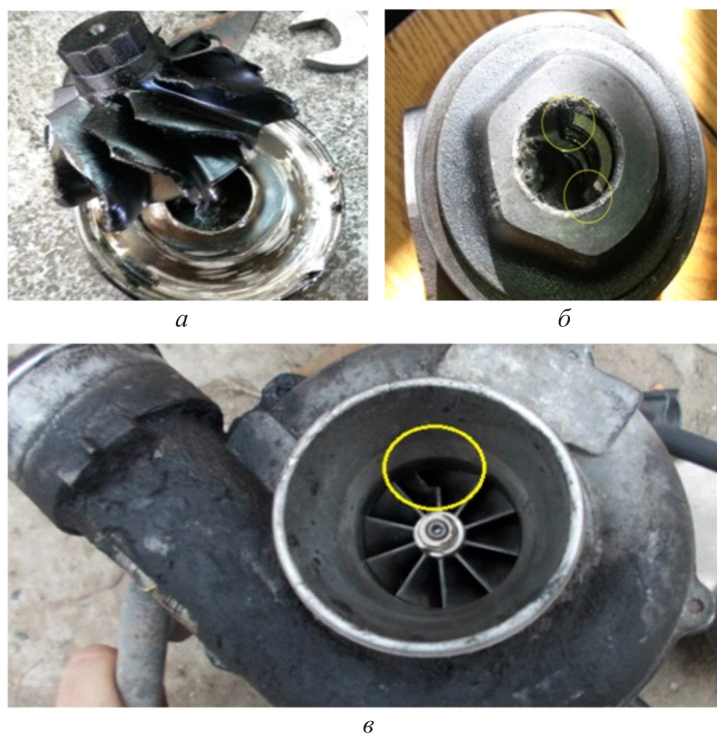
Разрушение деталей турбокомпрессоров ТКР 80.05.12:
